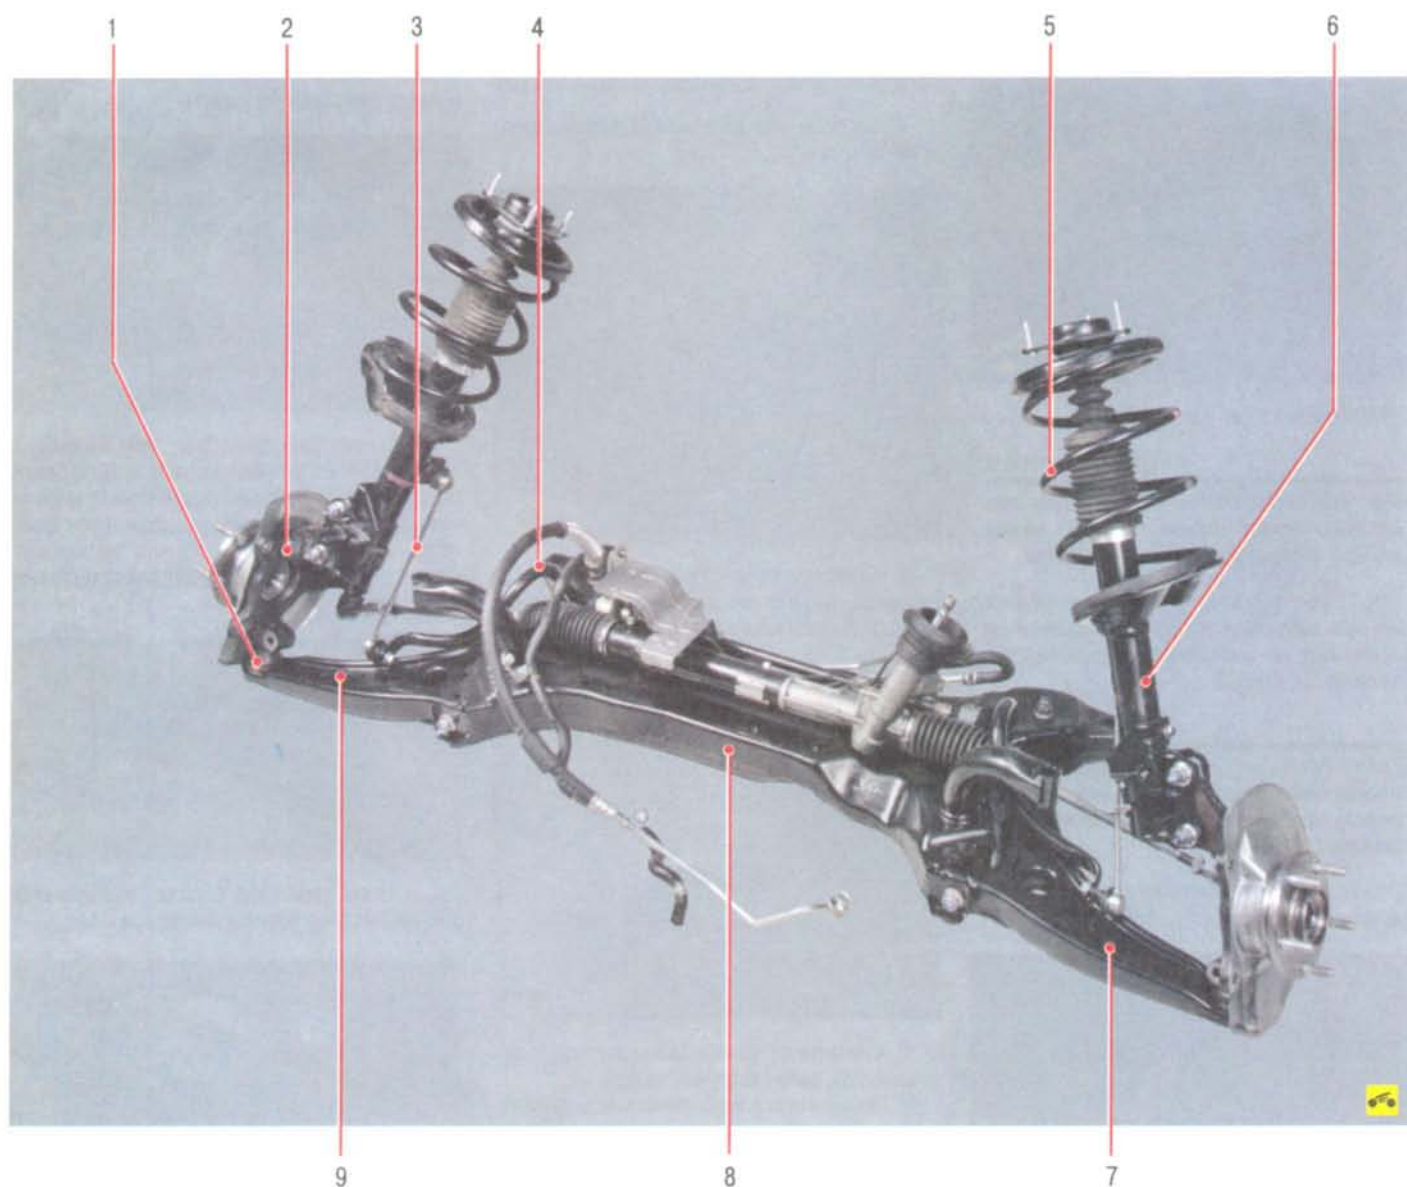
Передняя подвеска: 1 — шаровая опора; 2 — поворотный кулак; 3 — стойка стабилизатора поперечной устойчивости; 4 — стабилизатор поперечной устойчивости; 5 — пружина; 6 — телескопическая амортизаторная стойка; 7, 9 — рычаги; 8 — подрамник
